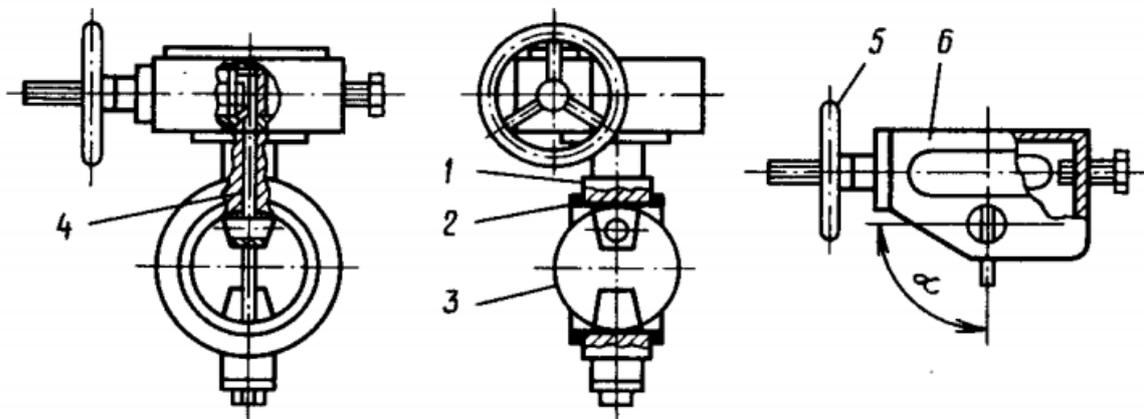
Конструктивная схема дискового поворотного затвора ($D_y = 200$ мм, $P_y = 1,6$ МПа): 1 — корпус; 2 — резиновая уплотненная муфта; 3 — диск; 4 — приводной вал; 5 — маховик; 6 — редуктор
